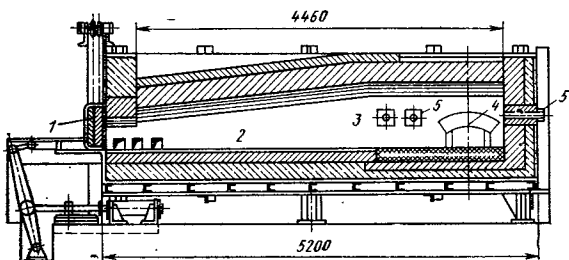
Полуметодическая толкательная печь для нагрева заготовок под штамповку:
